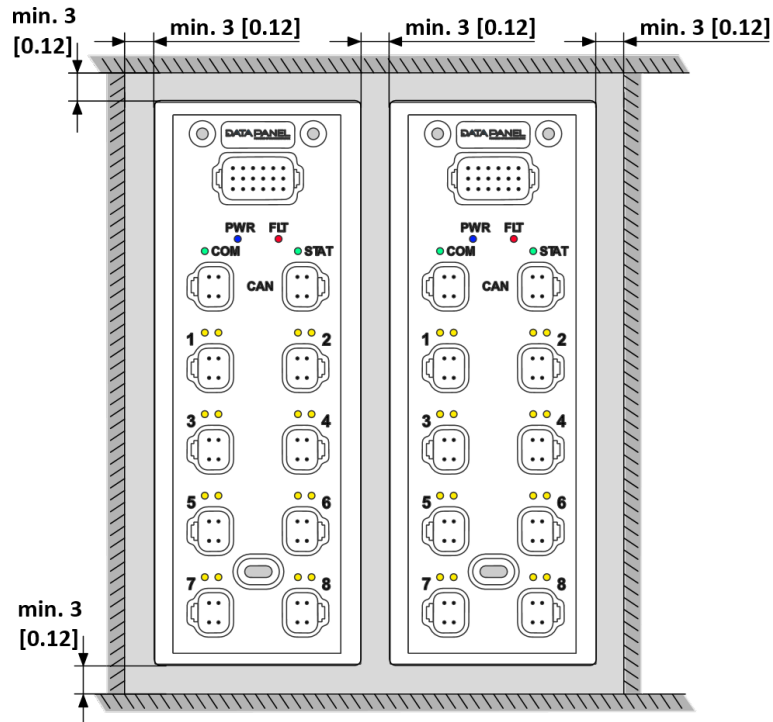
Montageabstände min. 3 mm (0.12 in)
